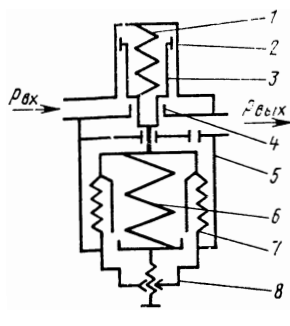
4. Схема регулятора давления обратного действия с разгрузкой:
